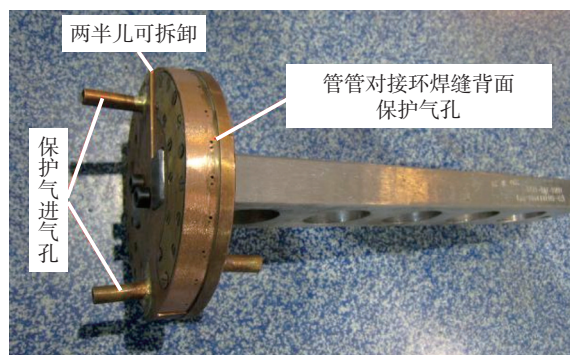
$\delta 1.0\text{mm}$ 导管焊接工装Fig.2 Welding jig of $\delta 1.0\text{mm}$ tube
